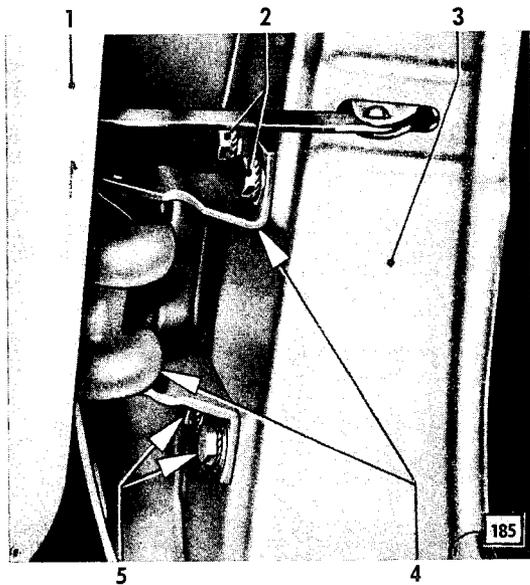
Befestigungsschrauben für Scharnier an Scharniersäule
